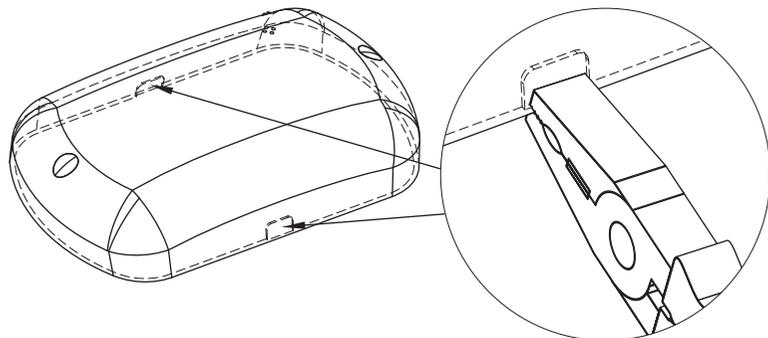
Расположение выламывающихся вставок в корпусе светильника SA-7206
